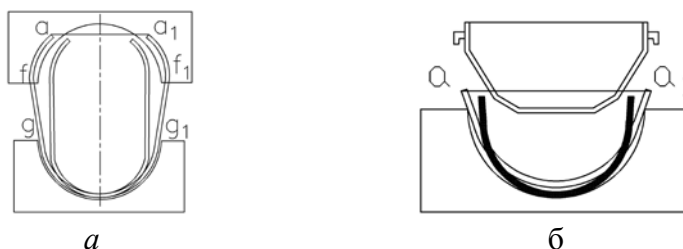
Относительное положение заготовки и инструмента в прессе окончательной формовки одношовной (а) и двухшовной (б) труб.
